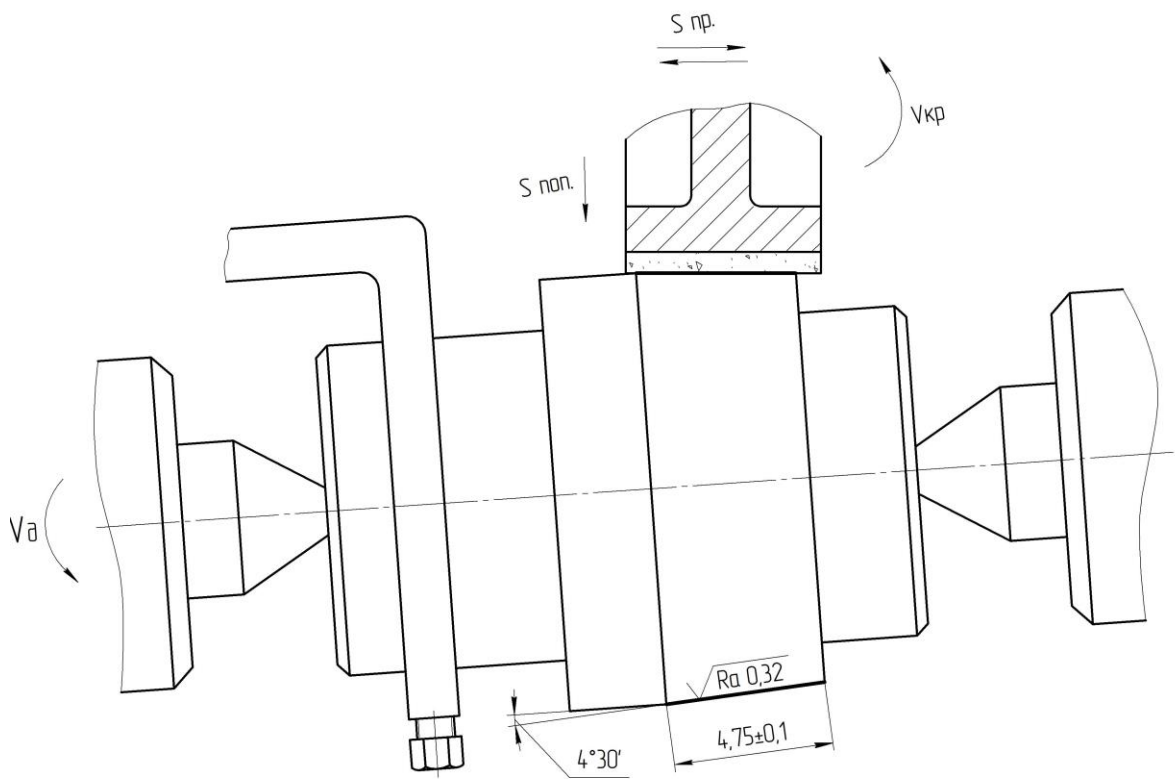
Схема обробки твердосплавного робочого елемента прошивки
